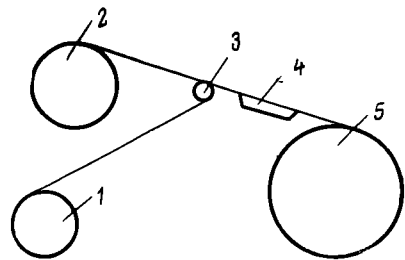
Схема подачи корда с питателя на сборочный барабан:
